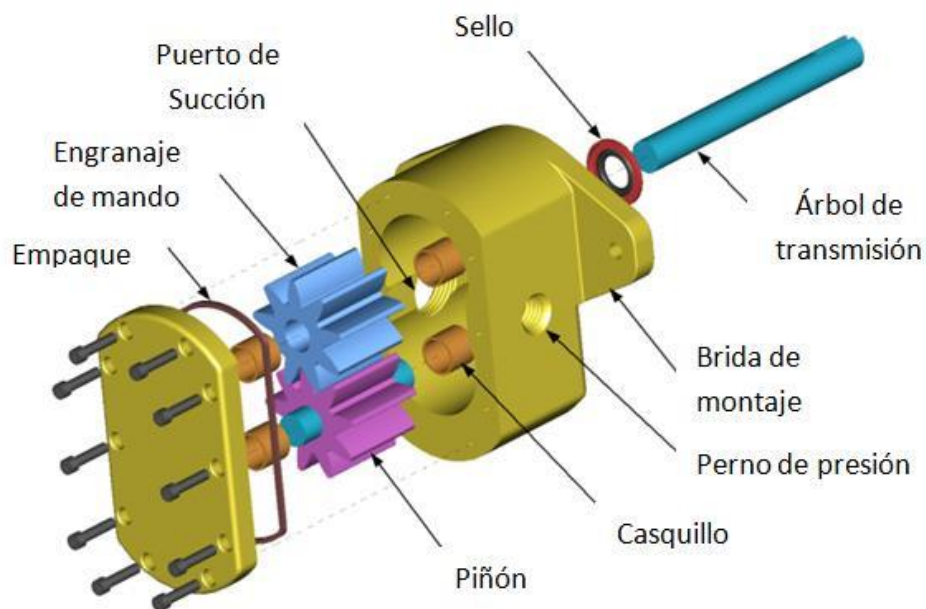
Despiece de un motor hidráulico ²¹
